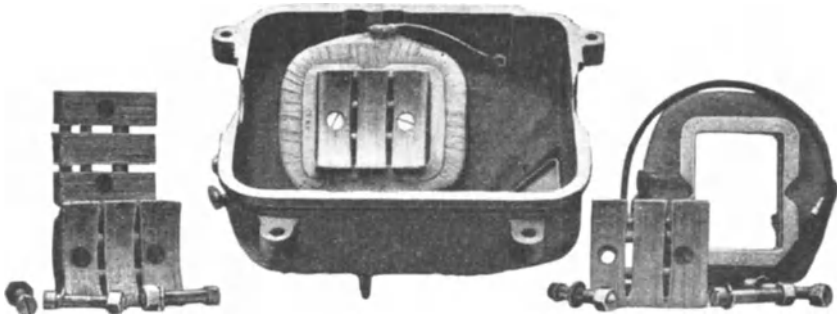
Gehäuseteile des Motors der English Electric Mfg. Co.
